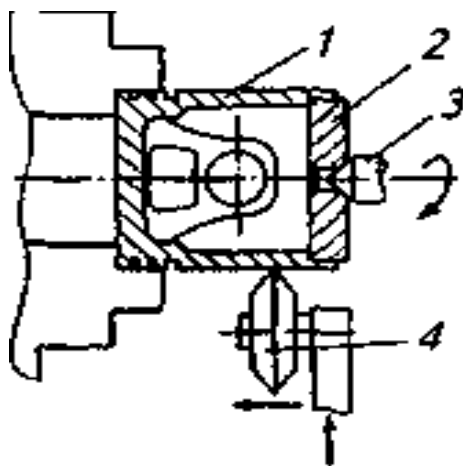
Установка поршня в токарному верстаті при накатці спідниці:
